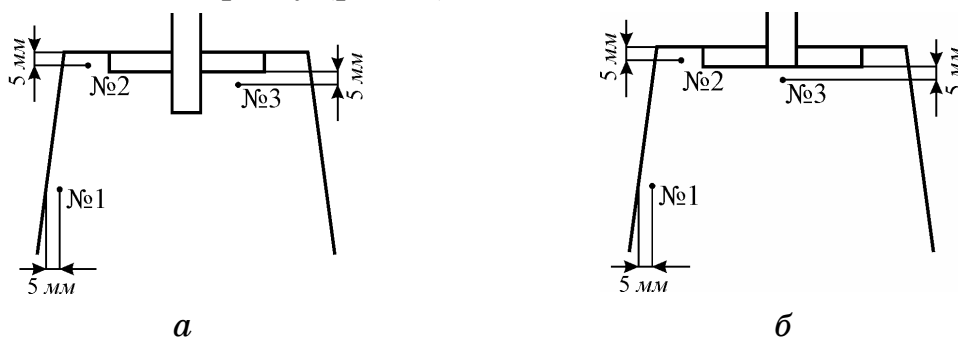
Схема цільнометалевого холодильника (а), корпусного холодильника з утеплювальною вставкою (б) та розташування термопар №№ 1 – 3
